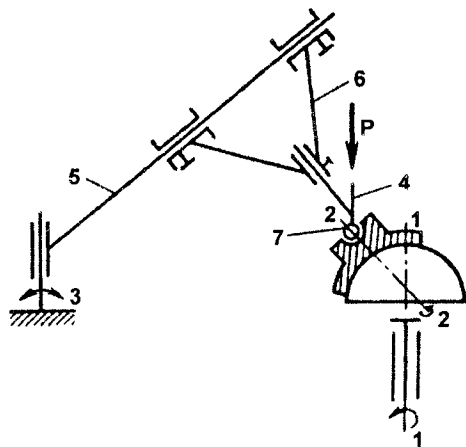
Кінематична схема обробки сферичної поверхні
